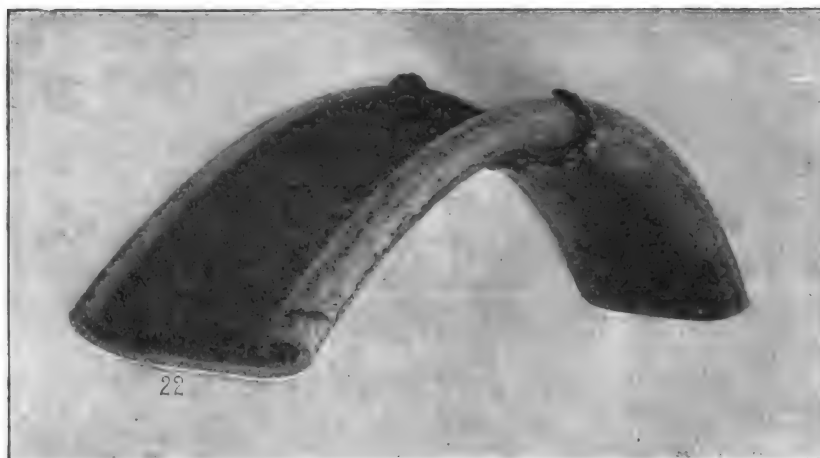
Jante soudée pour voiture automobile.
